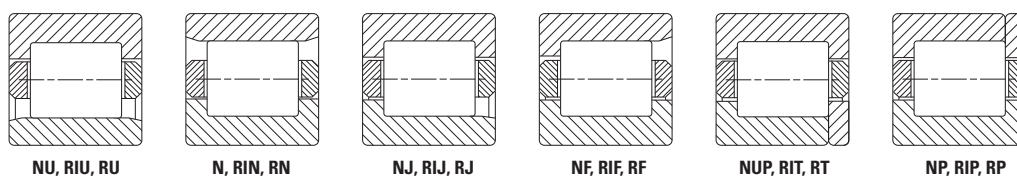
Cuscinetti a rulli cilindrici in dimensioni metriche ed in pollici serie standard.
